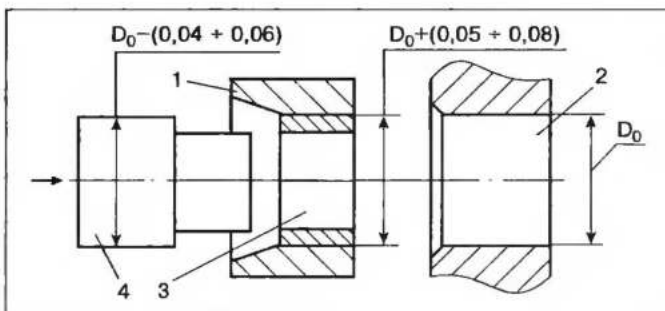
Схема запрессовки втулки, выполненной из двух половинок: 1 — оправка; 2 — опора; 3 — втулка; 4 — толкатель
